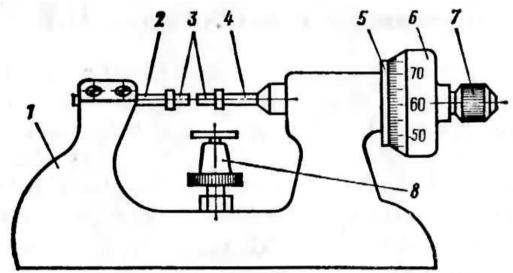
Общее устройство настольного микрометра: 1 – корпус; 2 – измерительная пятка; 3 – измерительные наконечники; 4 – подвижный измерительный стержень; 5 – стебель; 6 – барабан; 7 – фрикцион; 8 – измерительный стол
